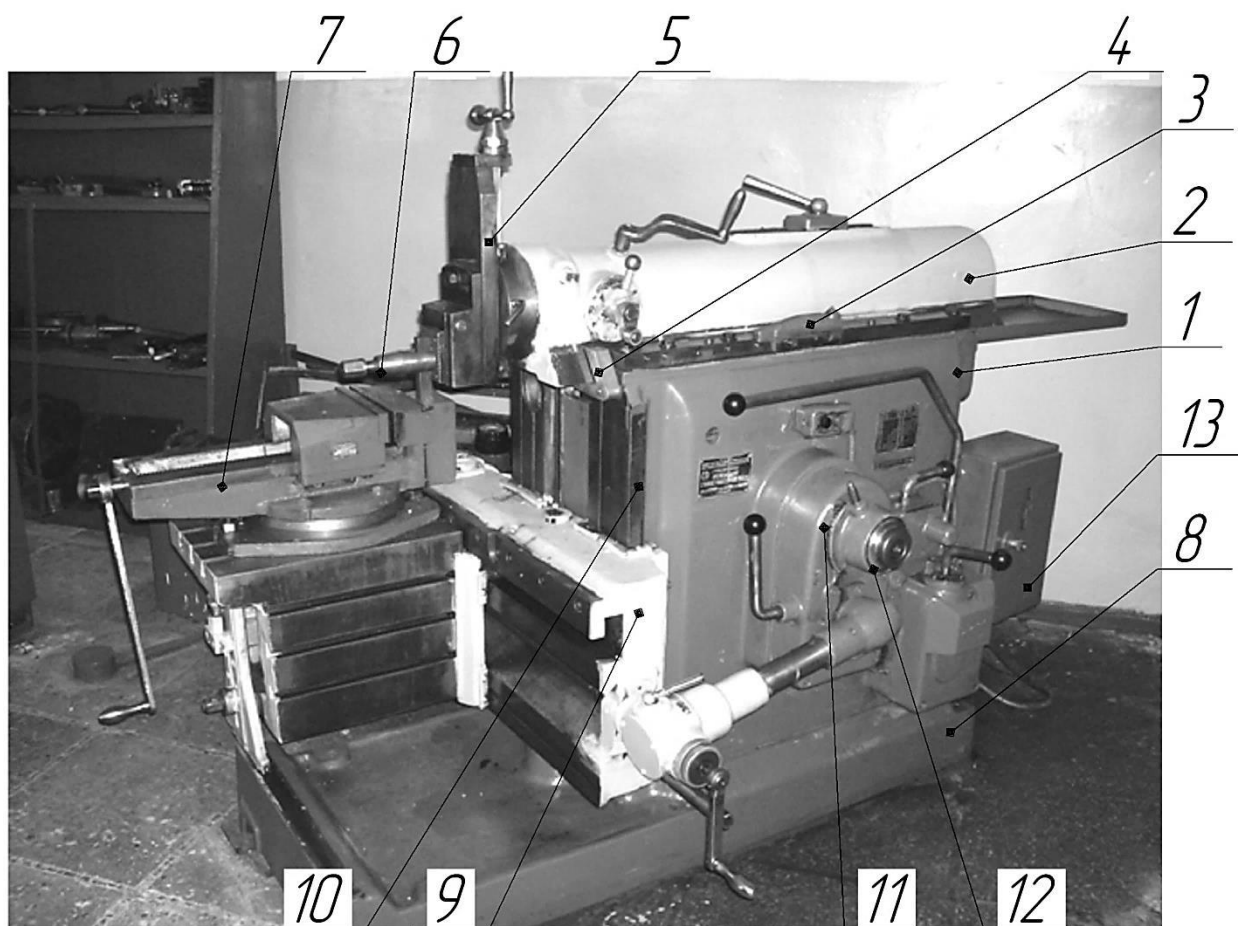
Общий вид станка: 1 – станина; 2 – ползун; 3 – упор неподвижный; 4 – направляющие горизонтальные; 5 – суппорт; 6 – резцедержатель; 7 – стол; 8 – стойка; 9 – поперечина; 10 – направляющие станины вертикальные; 11 – сектор контроля величины поперечной подачи; 12 – лимб контроля длины хода ползуна; 13 – электродвигатель
